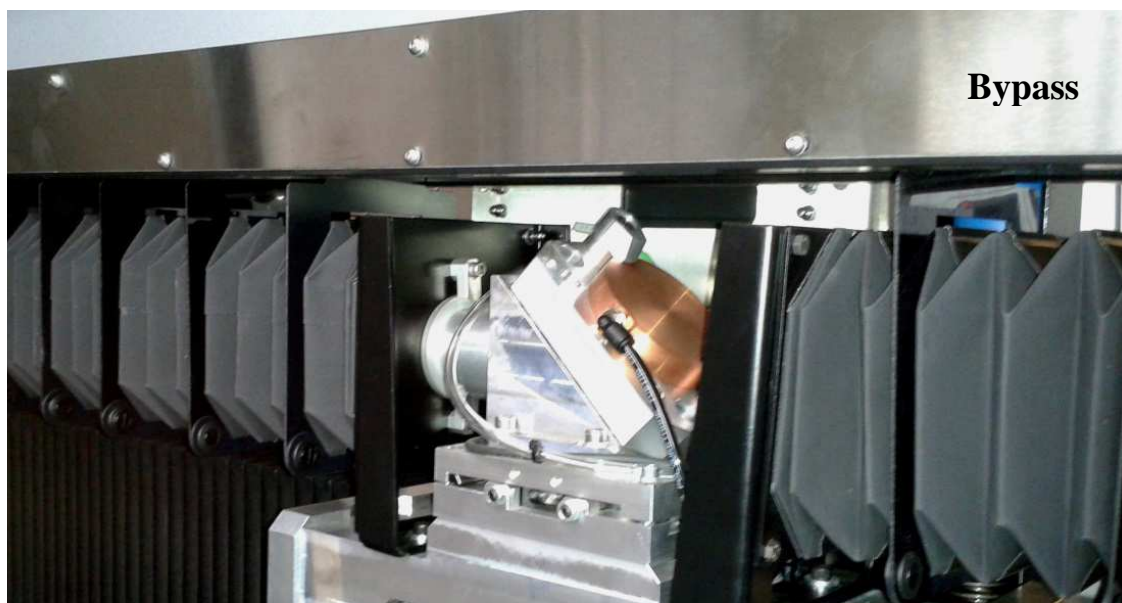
Bypass instalado por cima do fole para recirculação do ar
